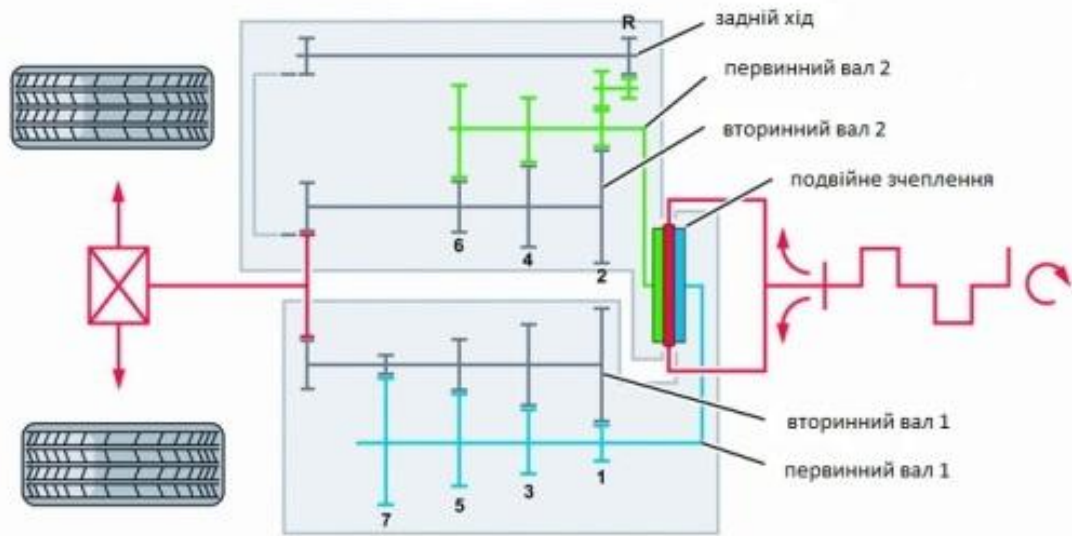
Принципова схема роботизованої коробки перемикання передач з двома зчепленнями
